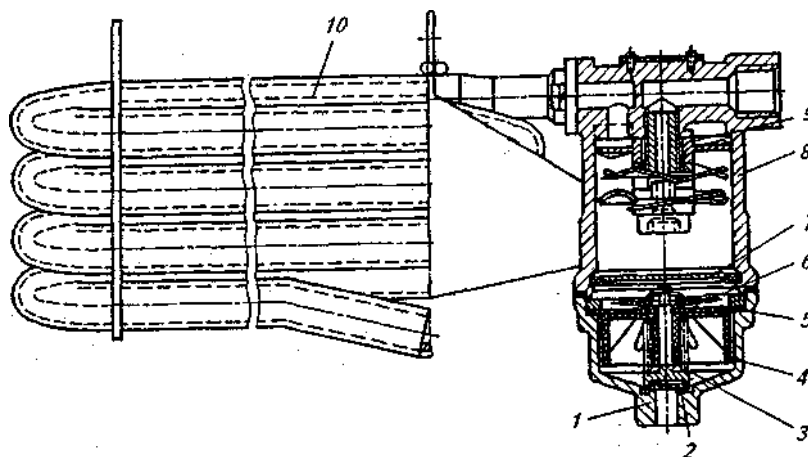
Влагоотделитель: 1 — корпус конденсатосборника; 2 — нижний клапан; 3 — пружина; 4 — поршень; 5 — диафрагма; 6 — верхний клапан; 7 — сетка; 8 — корпус; 9 — лепестковая шайба; 10 — охладитель
